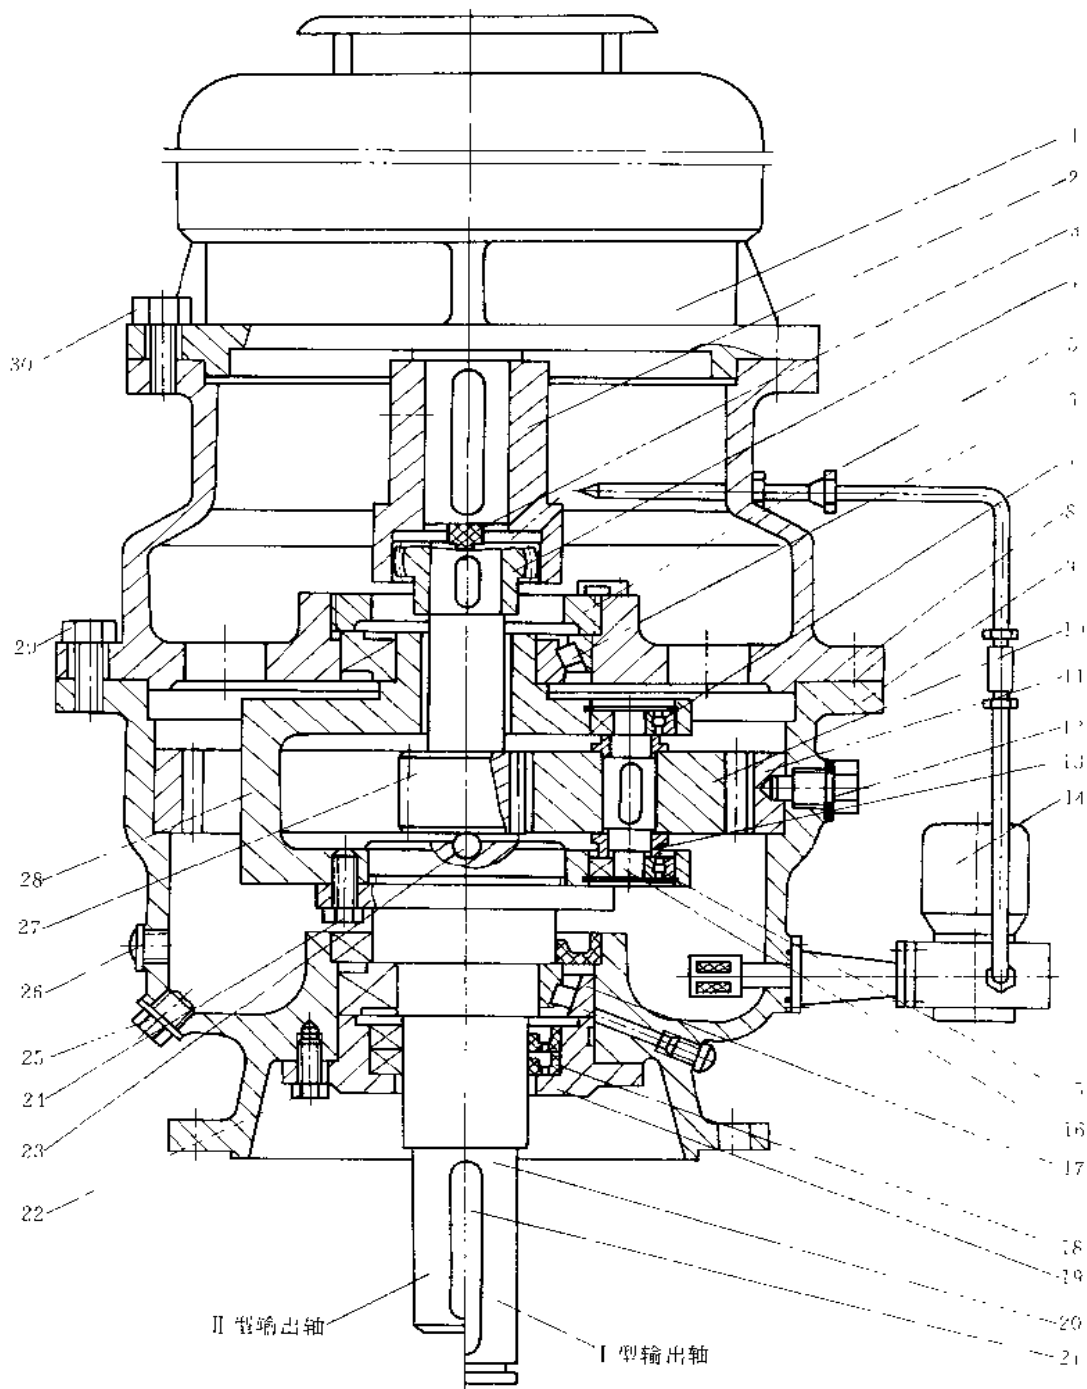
立式单级 NGW 型行星齿轮减速器
